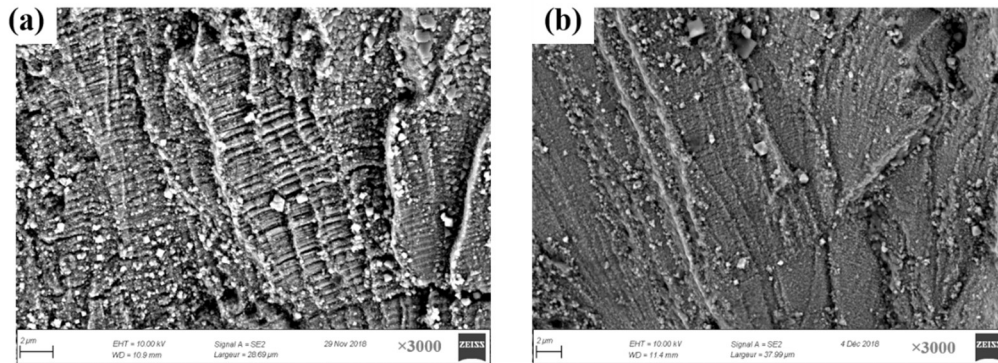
Stries de fatigue à 60 μm de profondeur, (a) éprouvette 743B-D (LVDT=1,4 mm), (b) éprouvette 743B-J (LVDT=1,1 mm)
